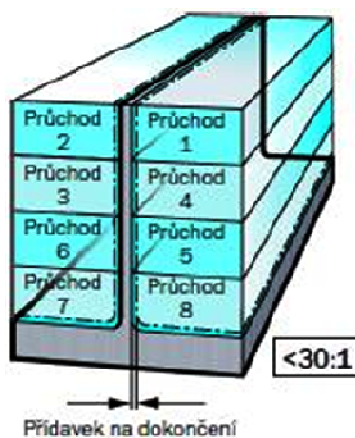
Obráběcí strategie zvaná “zik-zak” [10,28].
